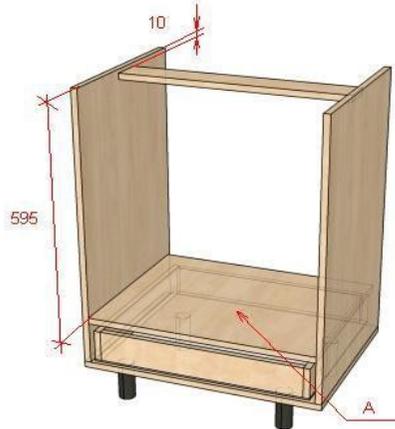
Короб под духовой шкаф и варочную поверхность
